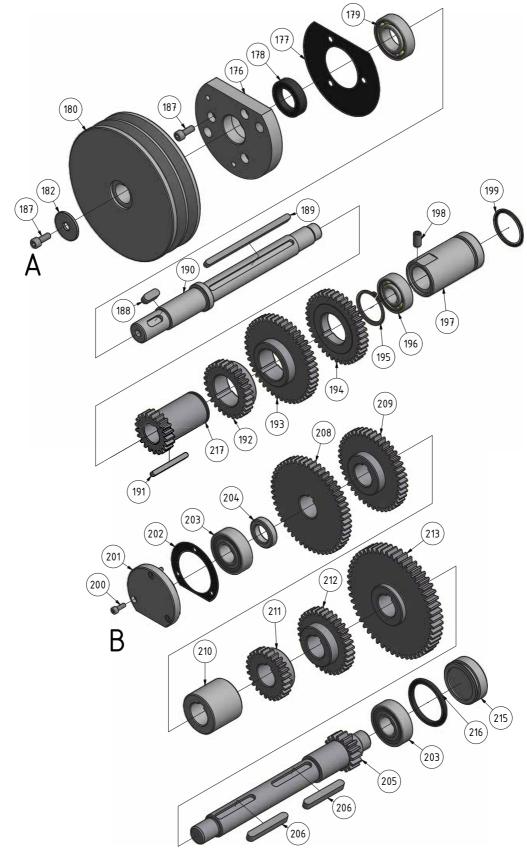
Getriebe Spindelstock 3-6 - Headstock gear 3-6
